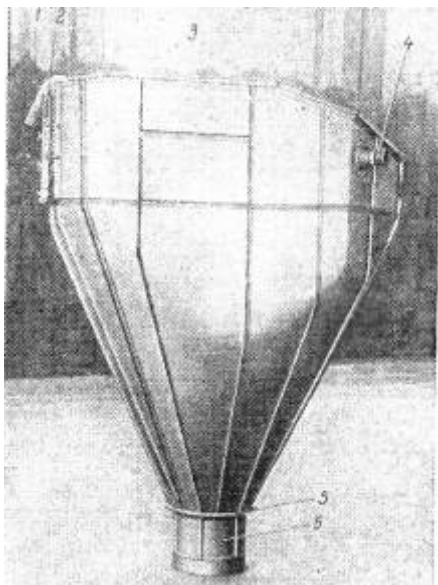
Бак для химикатов: 1 — заправочная труба; 2 — ремонтный люк; 3 — узел крепления бака к шпангоуту фюзеляжа; 4 — окуляр; 5 — фланец горловины бака; 6 — горловина бака
